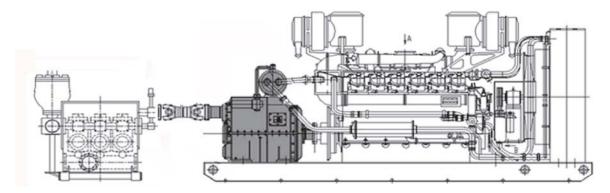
Рисунок внешнего вида установки редуктора обратного хода гидроагрегата моноблочного насоса
